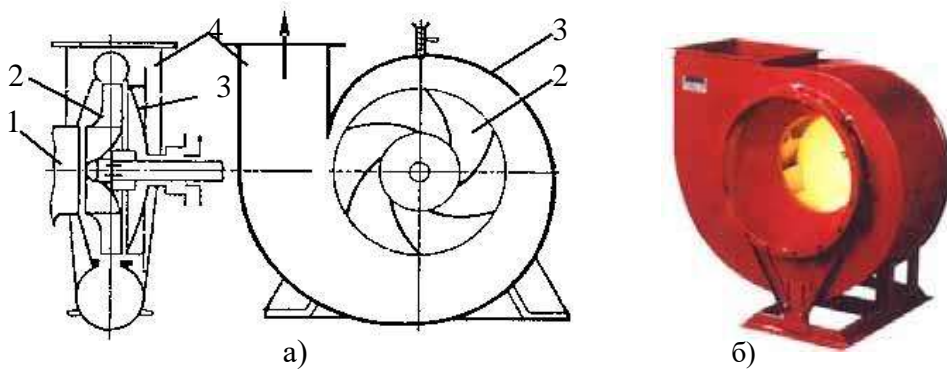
Конструкція (а) та зовнішній вигляд (б) відцентрового нагнітальника: 1 – всмоктувальний патрубок; 2 – робоче колесо; 3 – камера; 4 – нагнітальний патрубок
